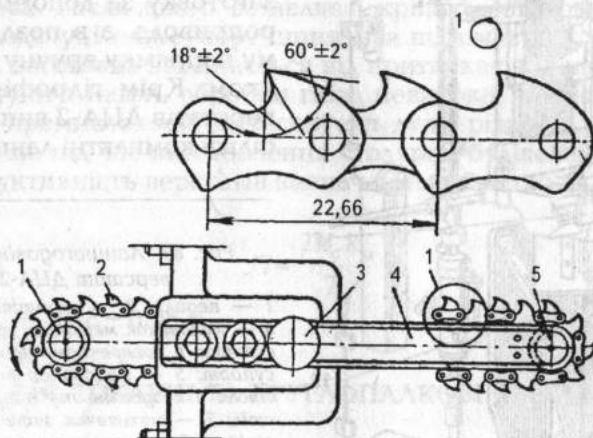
Фрезерний ланцюг для ланцюгодовбальних верстатів:
